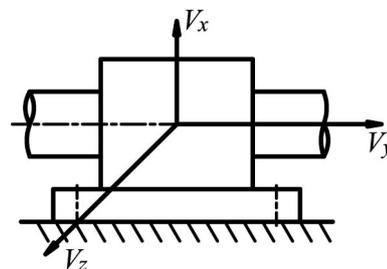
Общий вид опорного подшипника турбоагрегата:
